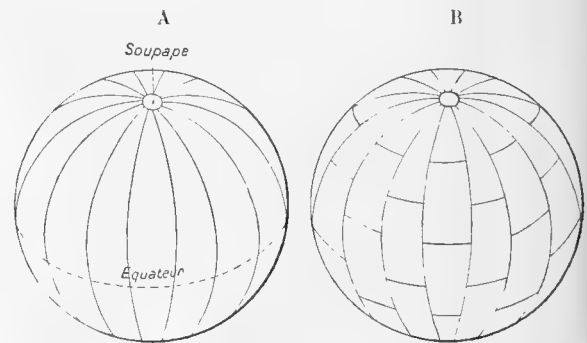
Modes de construction de l'enveloppe. — A, Tracé par fuseaux ordinaires ; B, Tracé par panneaux.
